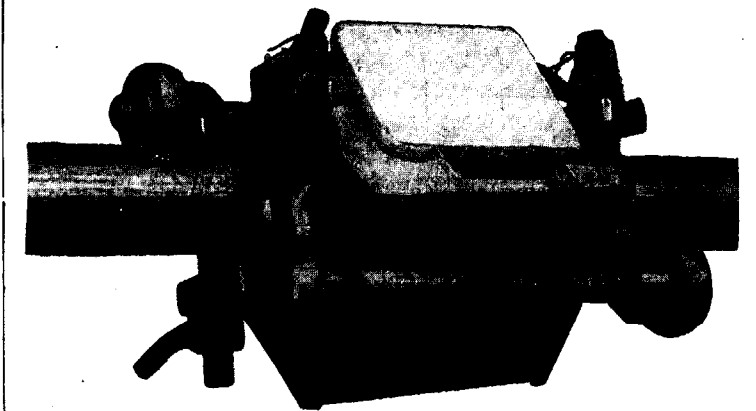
ª—Tubos horizontales preparados para la soldadura
